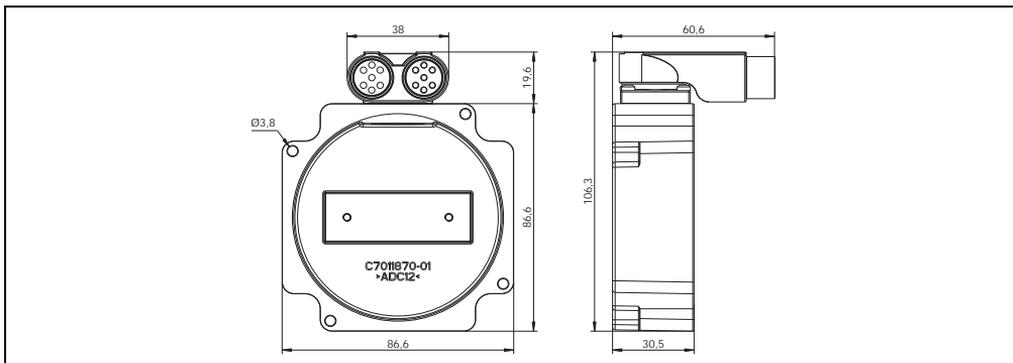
Schrittmotoren mit Hiperface IP65 Option - Abmessungen
